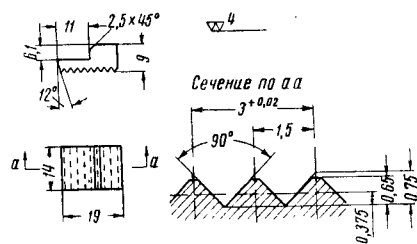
Стружколоматель к резцу конструкции С. Т. Полякова (деталь 5)
